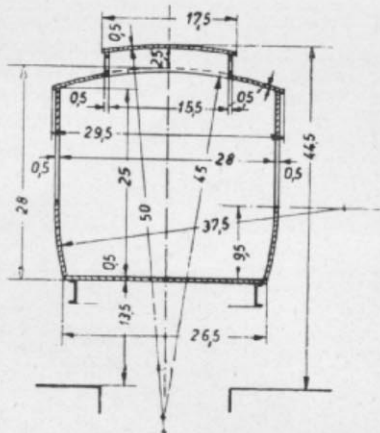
Wagenkasten-Seitenwand, Stirnwand und Dachbleche anfertigen. Seitenwand- und Dachaufbaufenster aussägen, Seitenwände ablegen.
